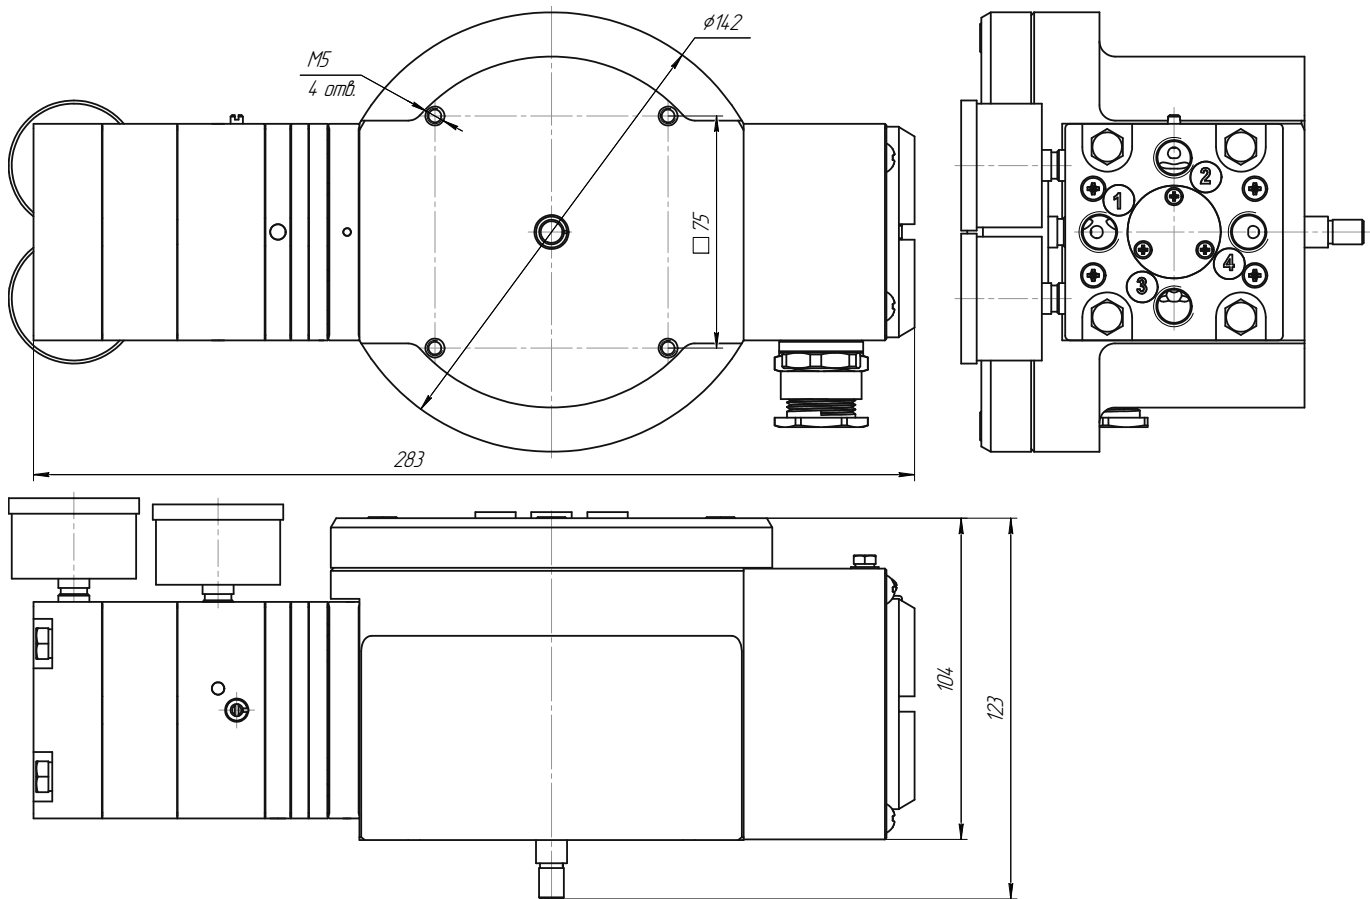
Габаритные, присоединительные и установочные размеры для позиционера двухстороннего действия с видом взрывозащиты «d»
